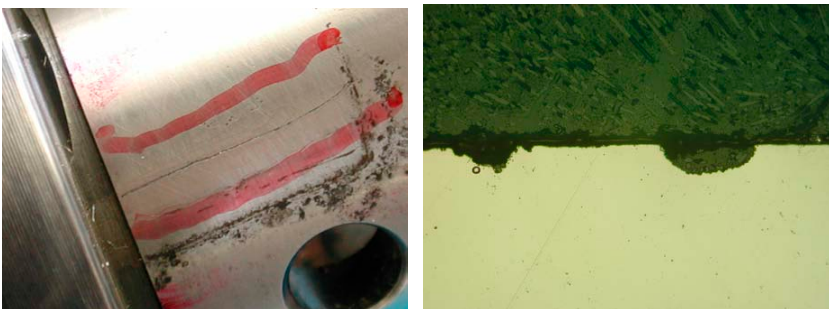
/4: Rissförmige Anzeige an einem Werkzeug ; Tatsächliche Schädigung durch eine sich linienförmig ausbreitende Muldenkorrosion
